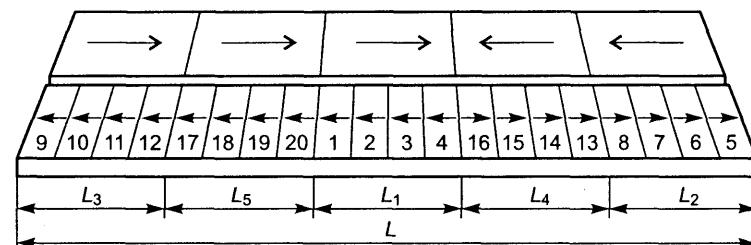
Сварка обратноступенчатым способом «вразброс»
